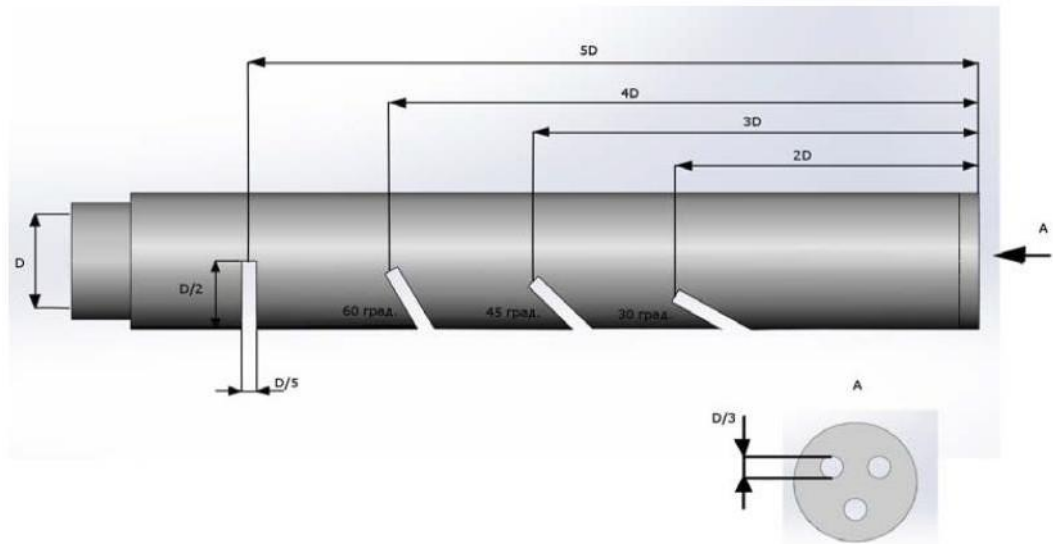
Насадка-распылитель для подачи газопорошкового огнетушащего вещества
